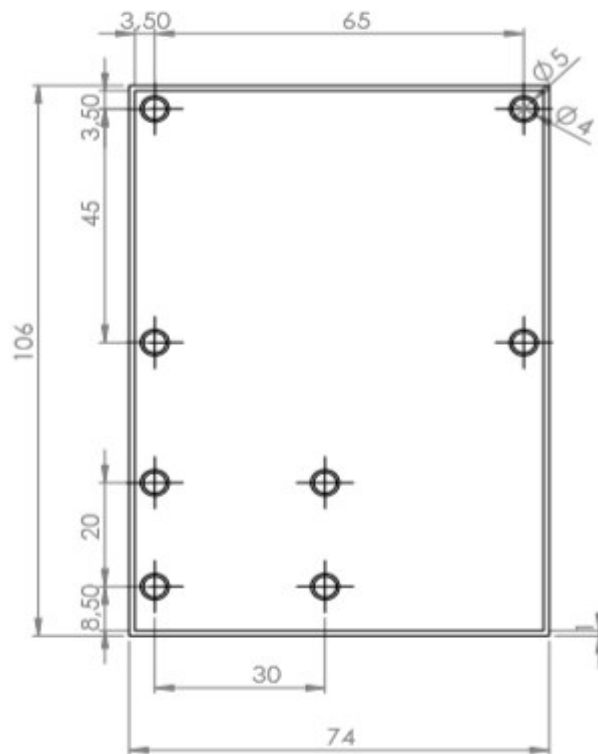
Vista frontal de la carcasa. Fuente: Autor
